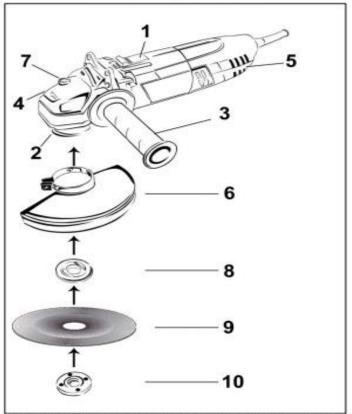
Общий вид УШМ с рукояткой «Компакт» (короткий и компактный корпус).
